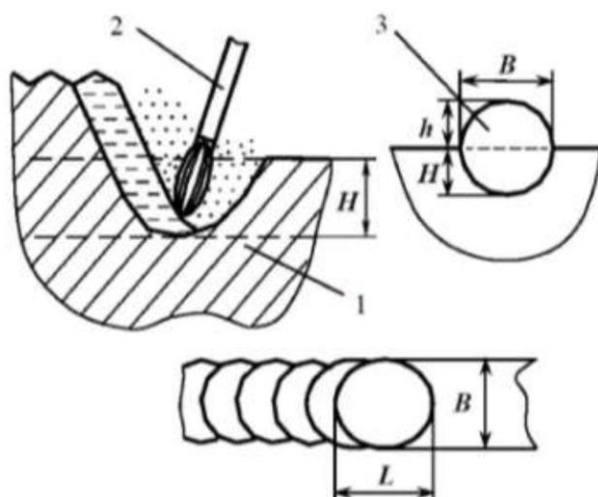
Общий вид сварочной ванны и наплавляемого слоя:
